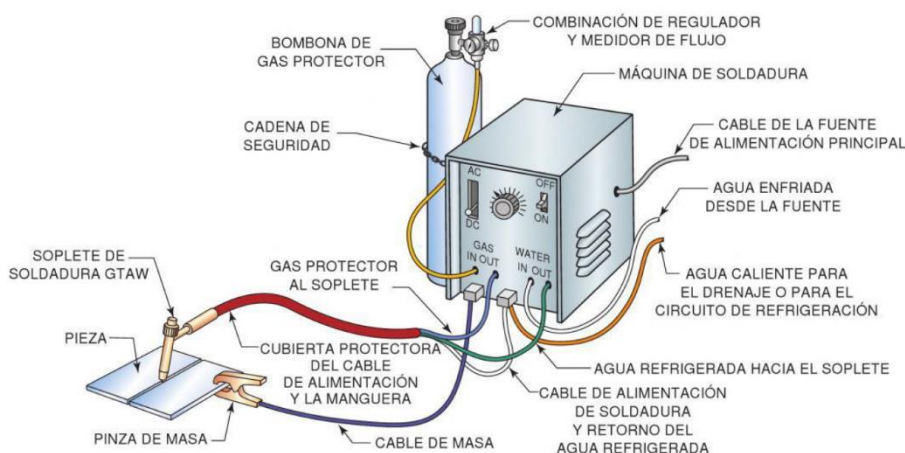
Equipo de soldadura GTAW. Fuente: Jeffus, L., 2009. Pág. 11. [22].
